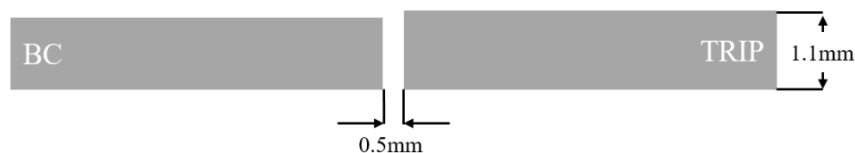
Diseño de la junta para la soldadura disímil.
